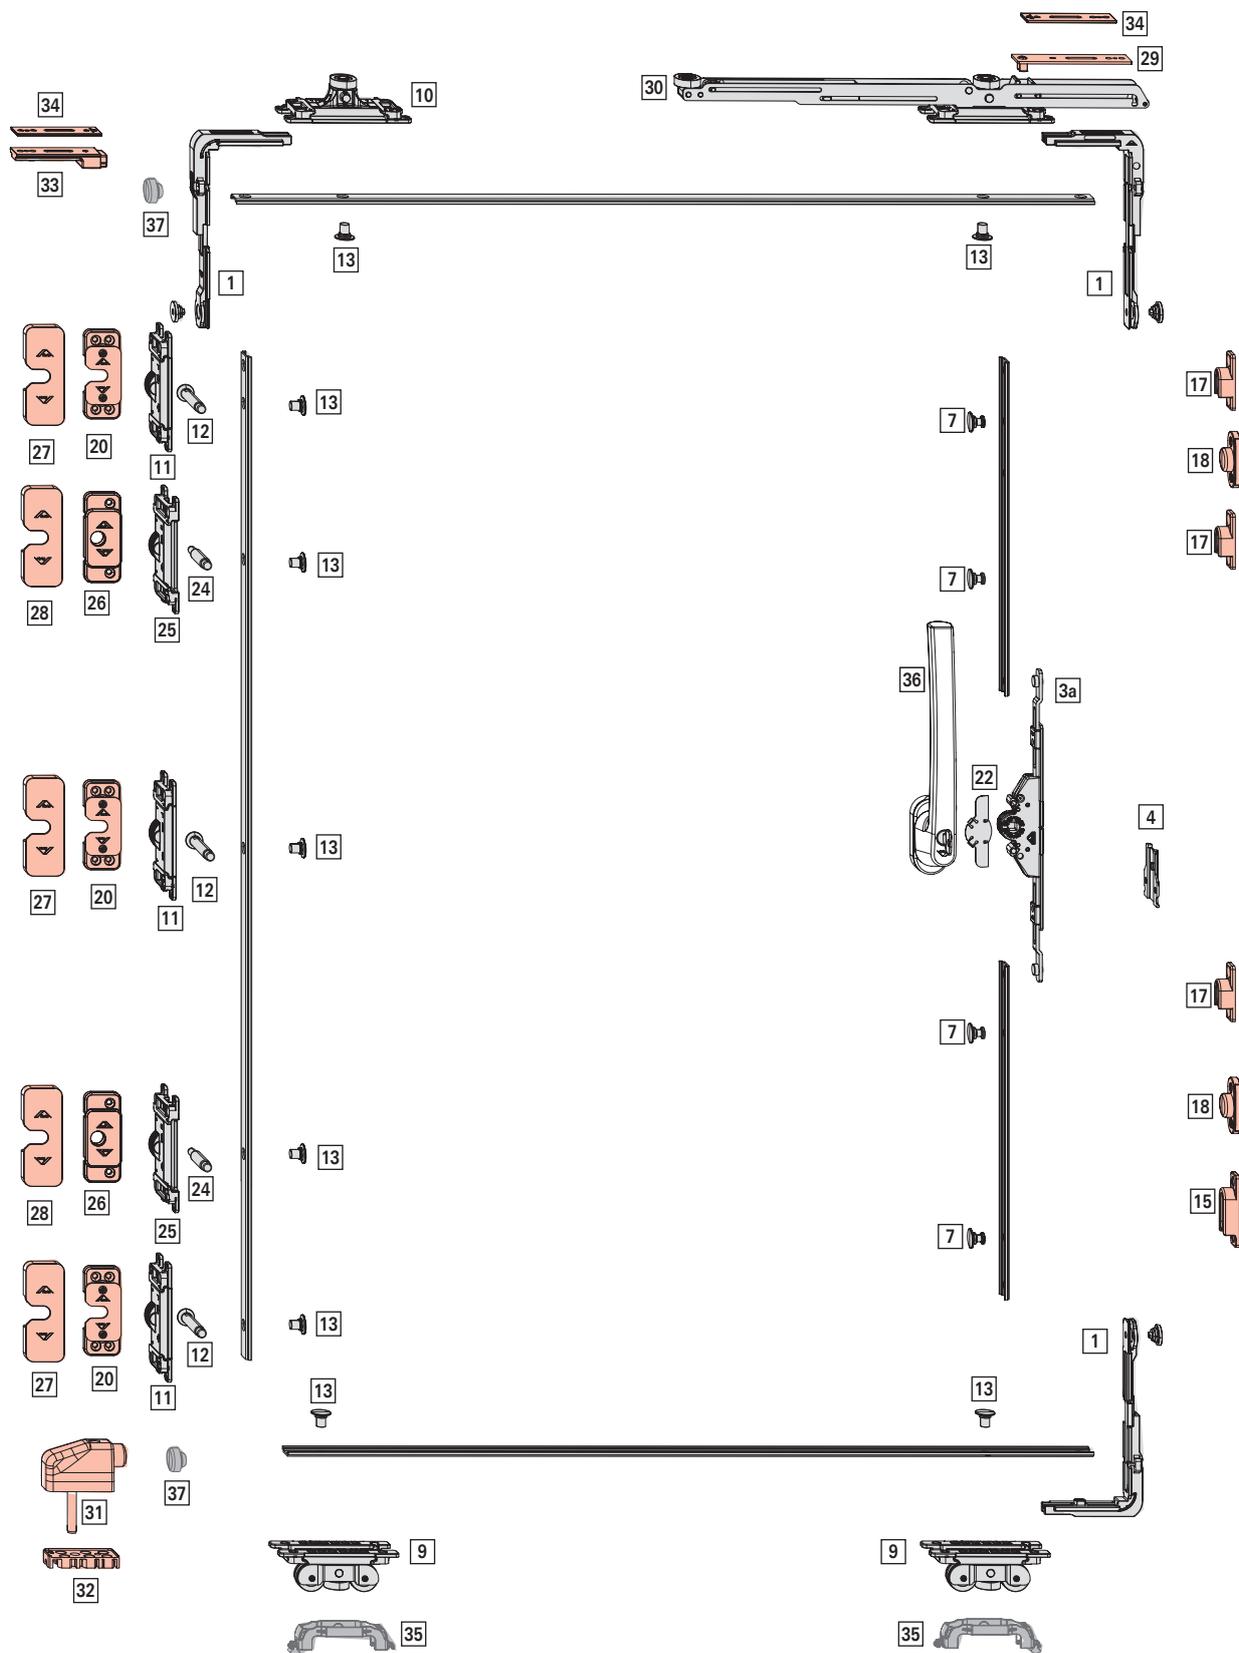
abgebildet: Ausführung DIN links; FB 900 mm; FH 1900 mm; Getriebe DM 25; RC 2
